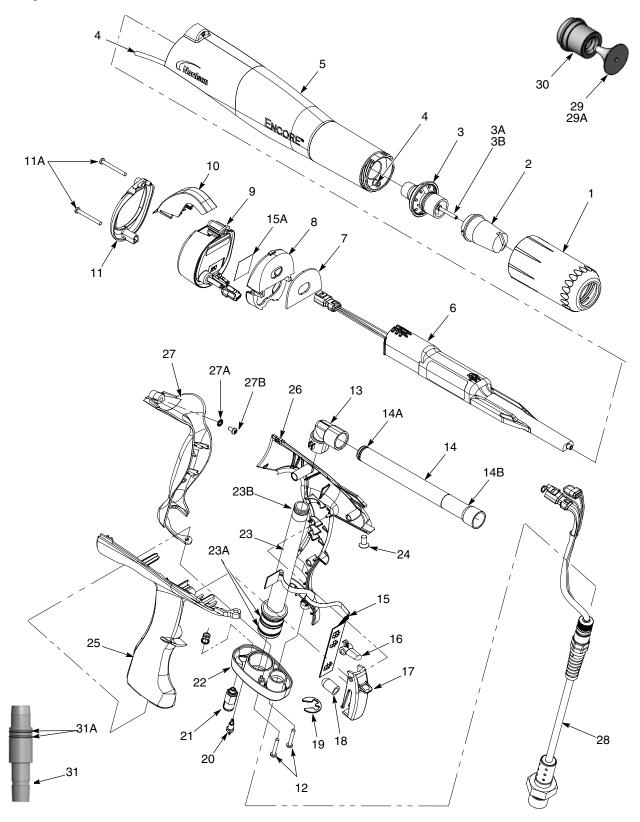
Vista explodida da pistola manual para pintura Encore e acessórios
